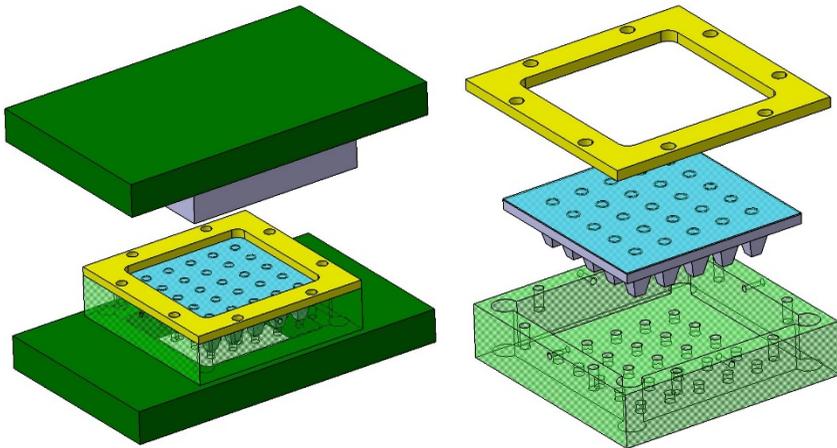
Konzept für erstes Demonstratorwerkzeug
